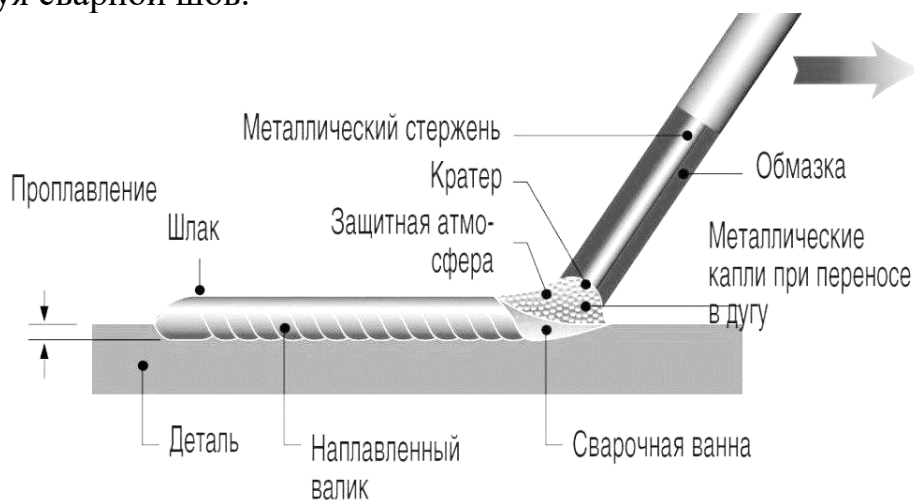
Схема процесса ручной дуговой сварки
